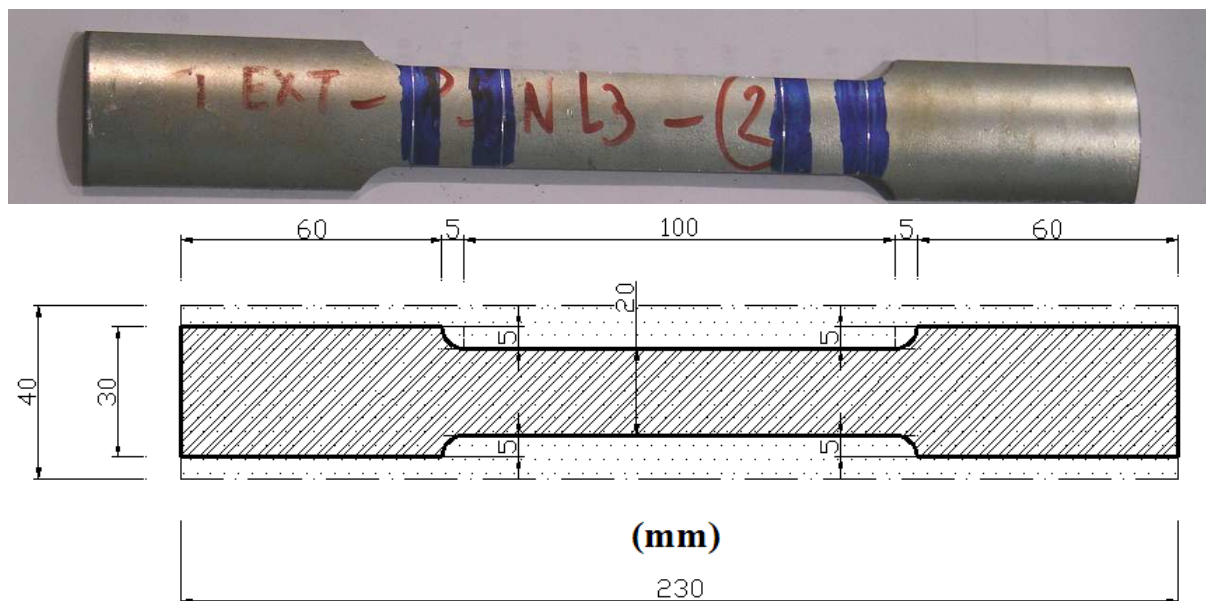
Aspecto geral e dimensões dos provetes maquinados.
